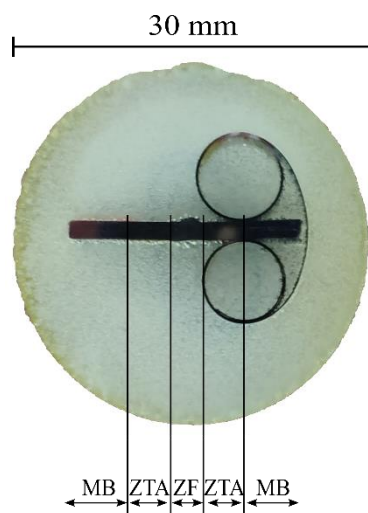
Seção transversal de uma amostra soldada.
